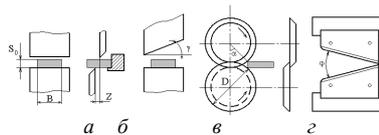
Схемы резки листового металла с помощью ножниц: а – ножницы с параллельными ножами; б – гильотинные ножницы; в – дисковые ножницы; г – вибрационные ножницы
